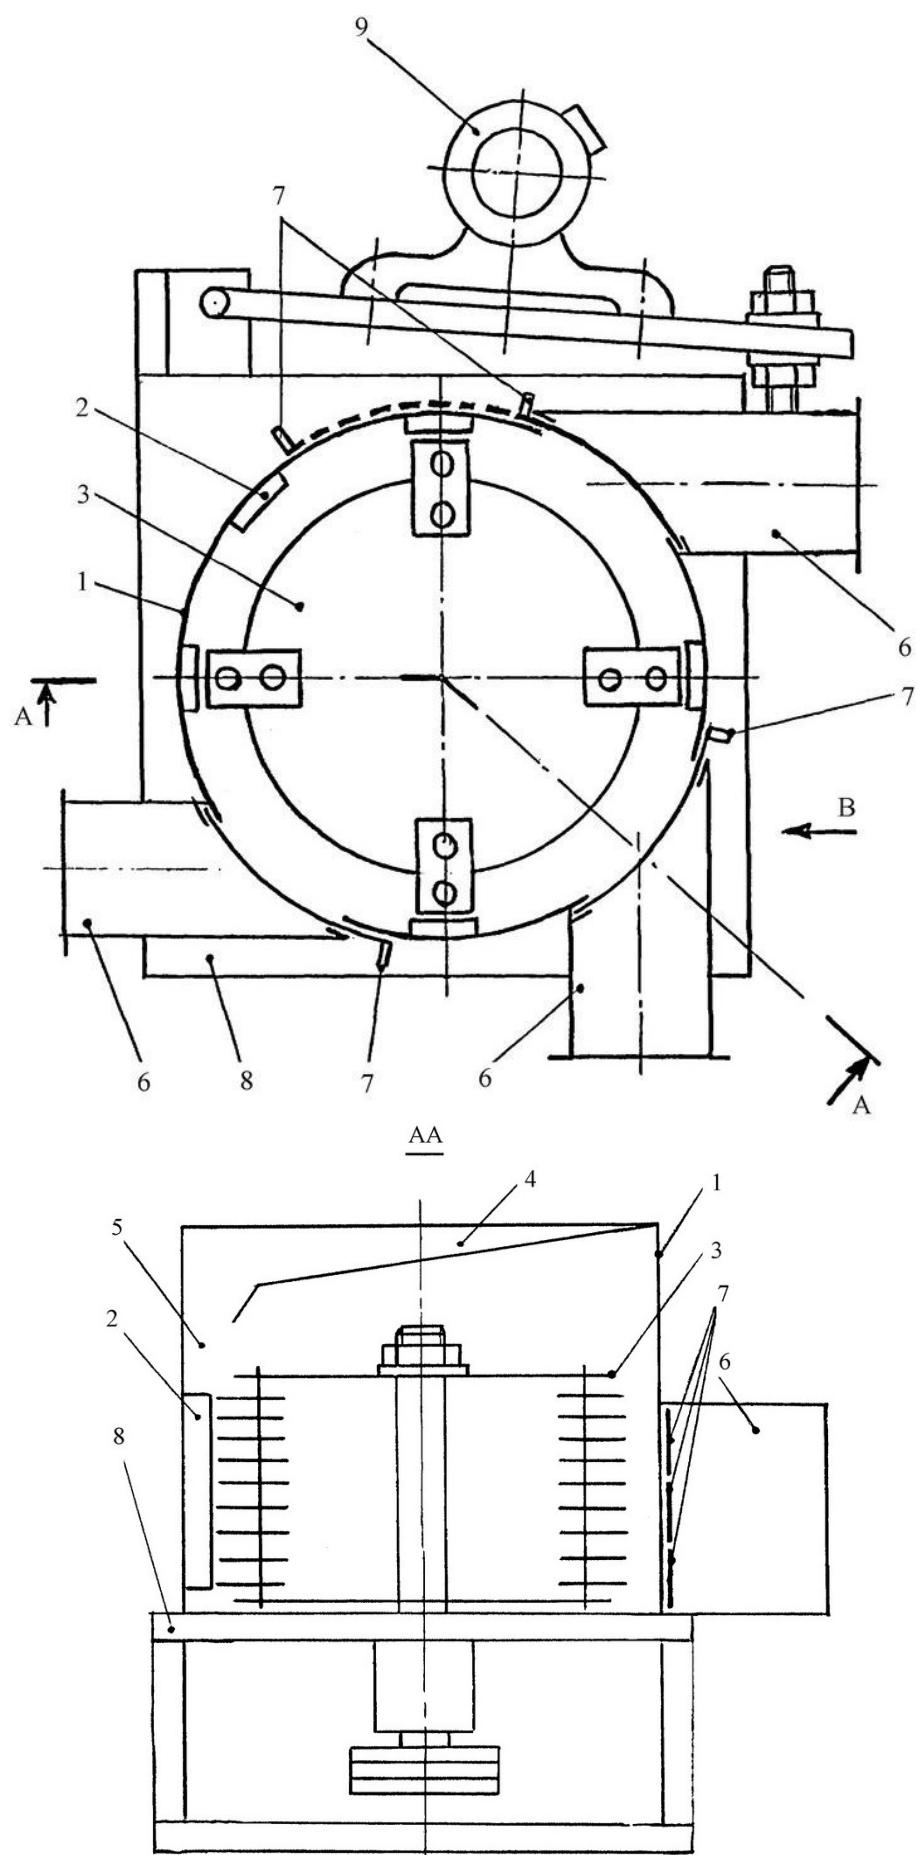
Общий вид дробилки молотковой по патенту РФ № 2236297
